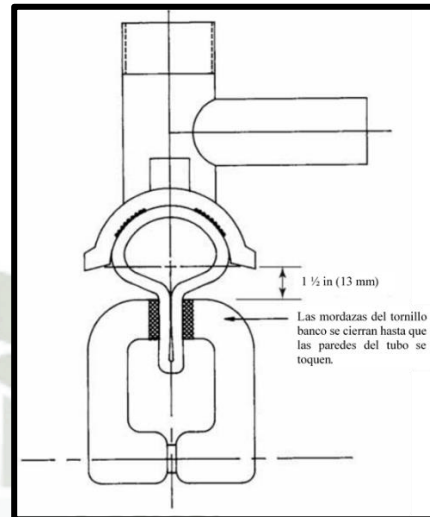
Ensayo de crunching test para un accesorio tipo silleta.
